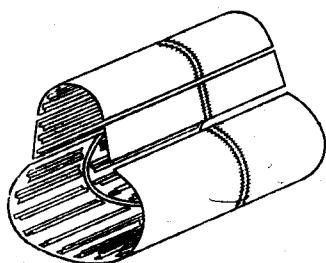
Членение отсека сварной конструкции, образованного сочетанием различных поверхностей.
